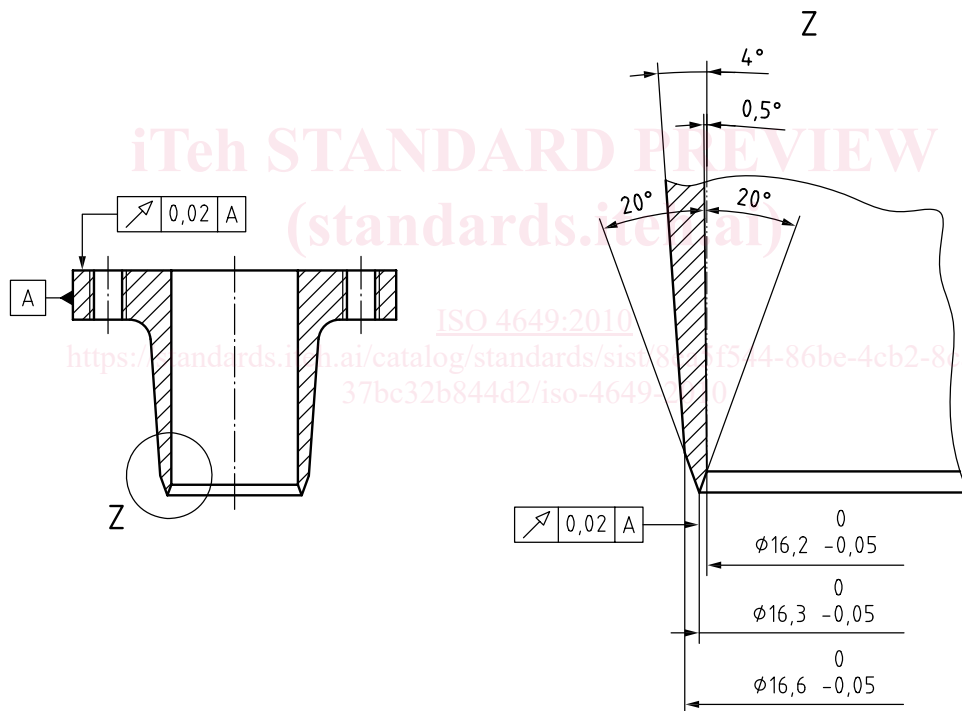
Пример полого сверла для подготовки испытательного образца
